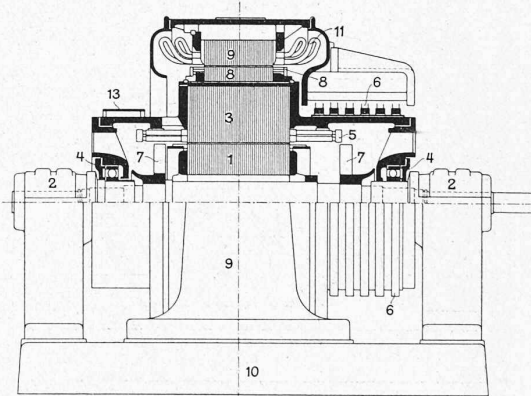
Typenskizze des Doppelrotor-Motors M. F. O.
